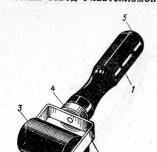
1 — крышка; 2—ручка; 3 — стержень; 4 — риска
